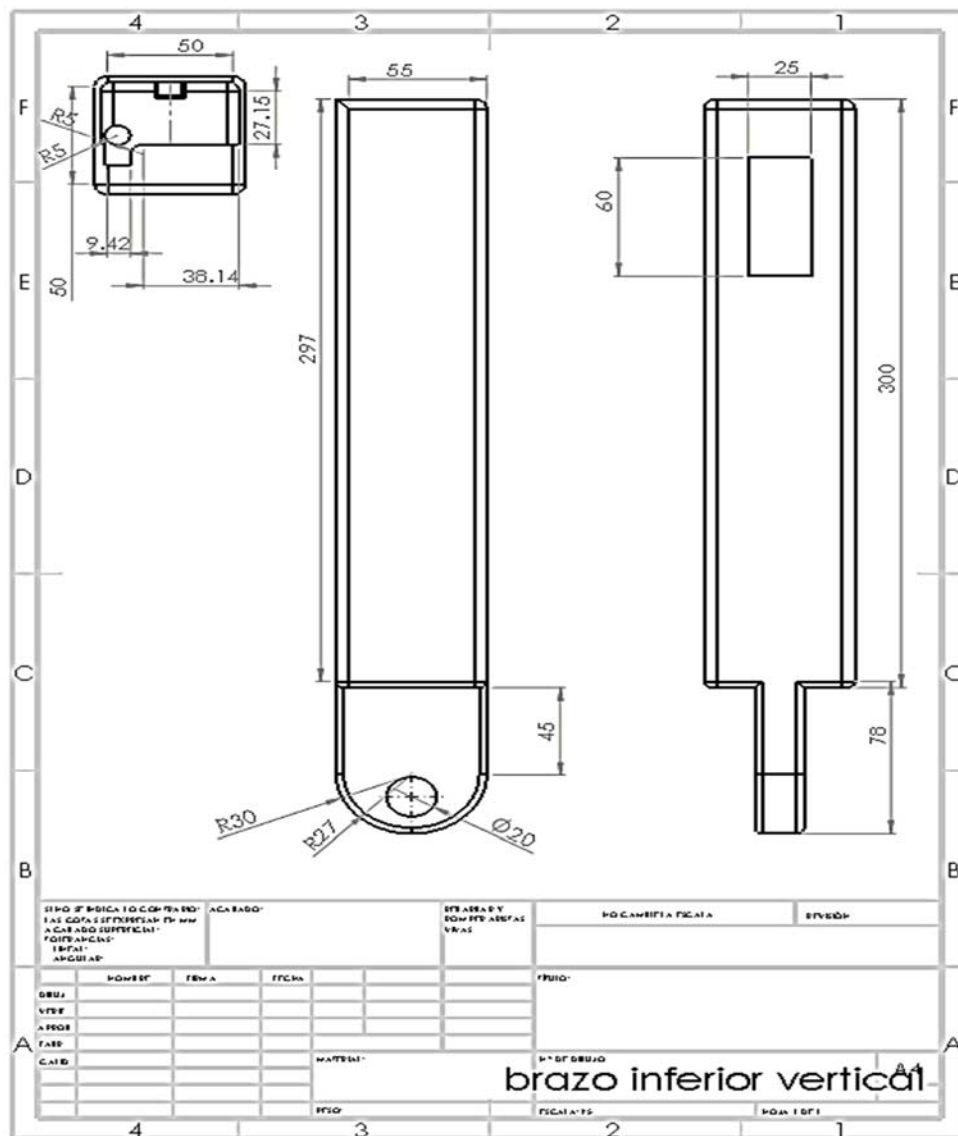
Plano de construcción de elemento de extensión vertical telescópica
